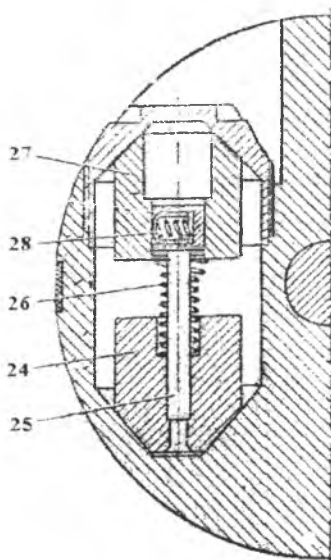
Стопорный механизм: 24, 27- конусы стопорного механизма; 25- шток; 26- пружина; 28- фиксатор
